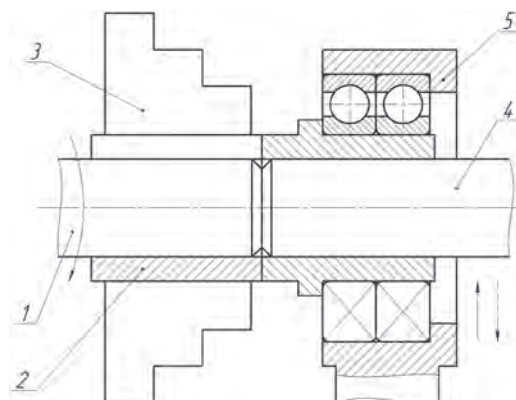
Схема устройства для разделения прутка на мерные заготовки в токарном станке: 1 – пруток; 2 – разрезная втулка; 3 – патрон; 4 – отделяемая заготовка; 5 – шариковая головка
